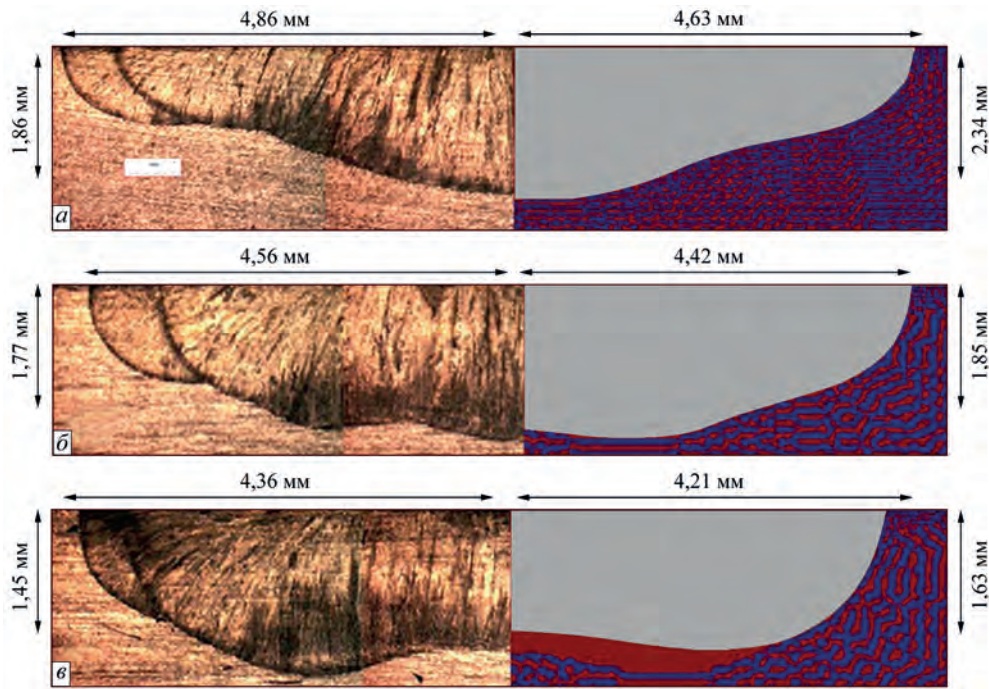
Макрошліфи зварних точок (зліва) і розрахункові форми проплавлення металу (праворуч) при точковому TIG зварюванні зразків зі сталі AISI 304 з низькочастотною модуляцією струму в діапазоні: а – 80...200; б – 100...180; в – 120...160 А [11]
